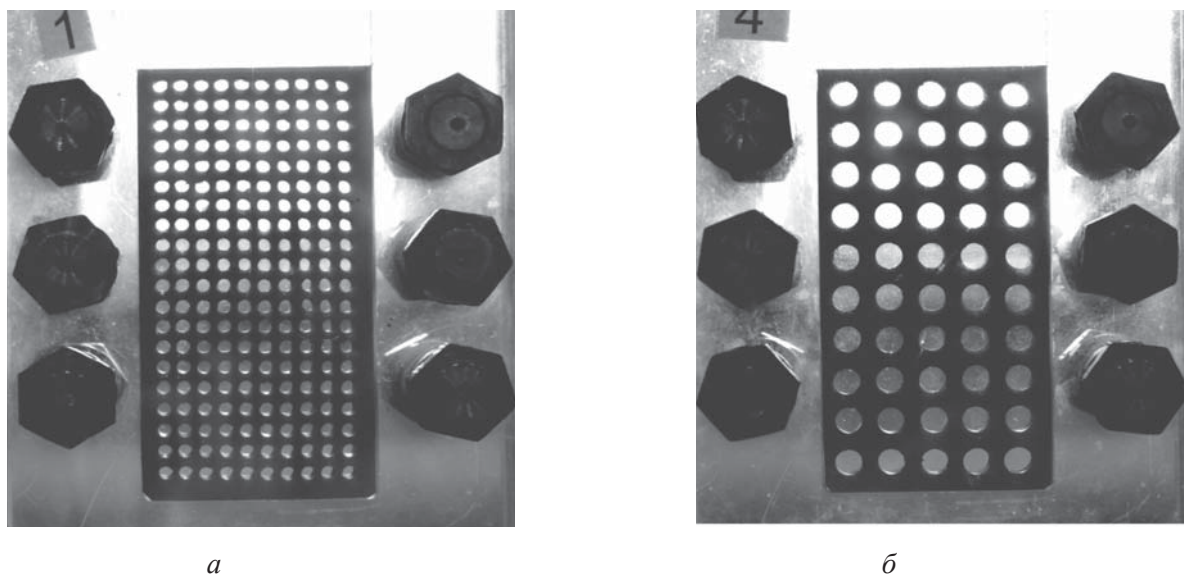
Внешний вид матрицы (штампа) с образцом:
